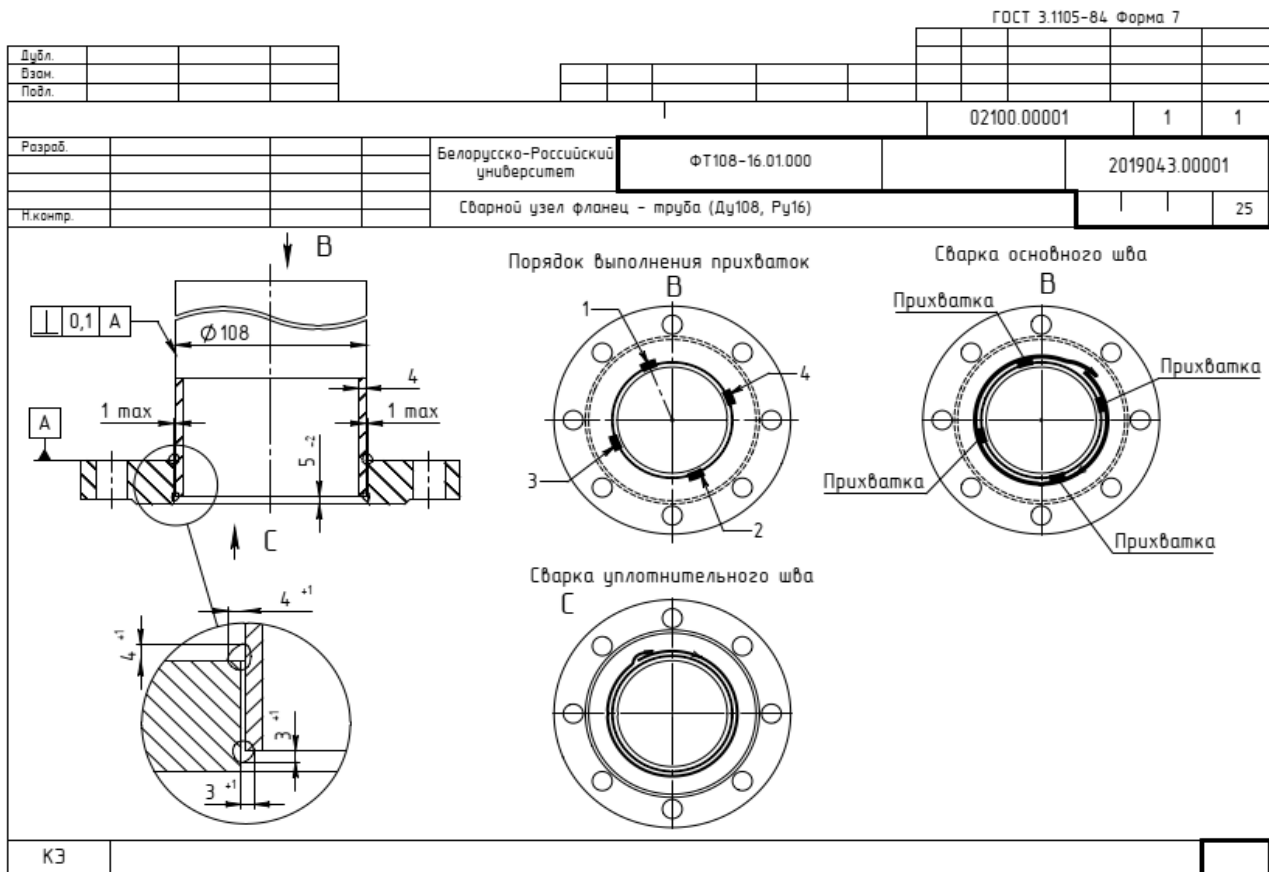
Пример оформления карты эскизов к сварочной операции
